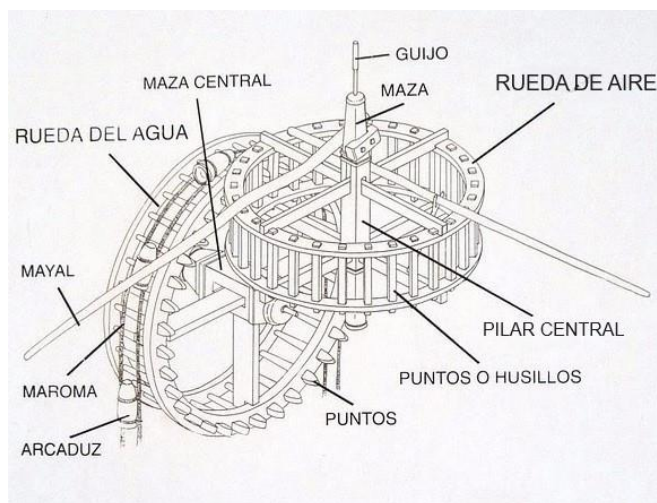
Esquema de noria tradicional de sangre restaurada en Rodalquilar (Almería). Fuente: Junta de Andalucía
